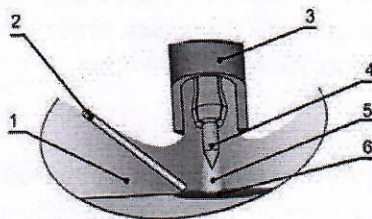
Схема ручной аргонодуговой сварки:
